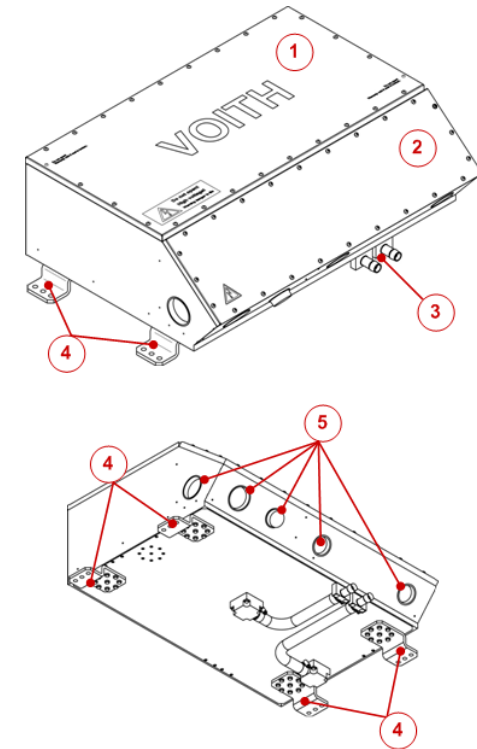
VHC Gehäuse und Anbauteile / VHC housing and attachments
